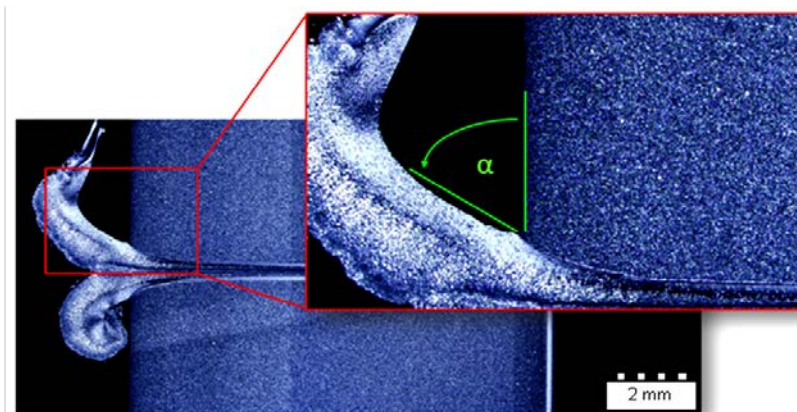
Geometrische Kerbe einer Vibrations-Schweißverbindung aus PP-H (Extrusionsplatte, Dicke 10 mm, Schweißweg 1,2 mm, Schweißzeit 15,28 s, Fügedruck 0,5 N/mm², Amplitude 0,9 mm)
